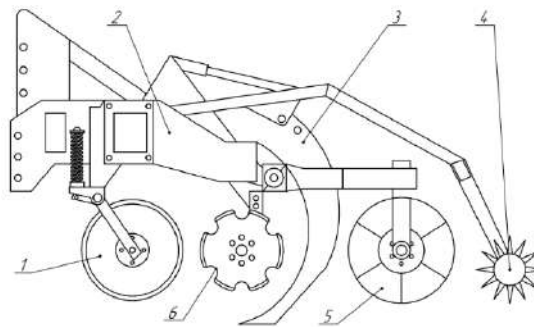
Схема секції культиватора для смугової обробки Stripcat:
